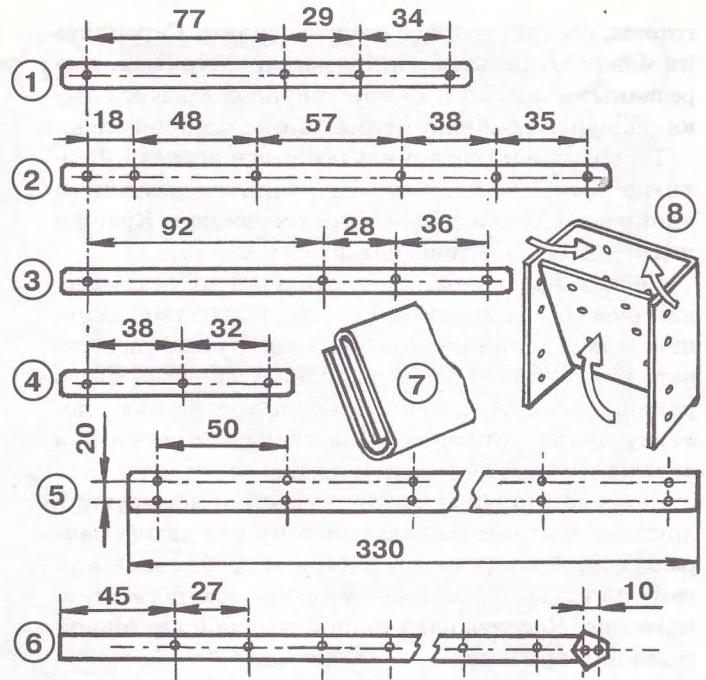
Основные размеры крепежных ремней доспеха: 1, 2, 3, 4 — кожаные полосы верхней части, ширина заготовки 6 см (свернуть втрое); 5 — поясные сегменты, 6 шт., ширина заготовки 9 см (свернуть втрое); 6 — полосы фартука, ширина заготовки 7 см (свернуть втрое); 7 — заготовка, свернутая втрое; 8 — кожаные накладки крепления полос к пластине (клапаны загнуть по стрелкам).
